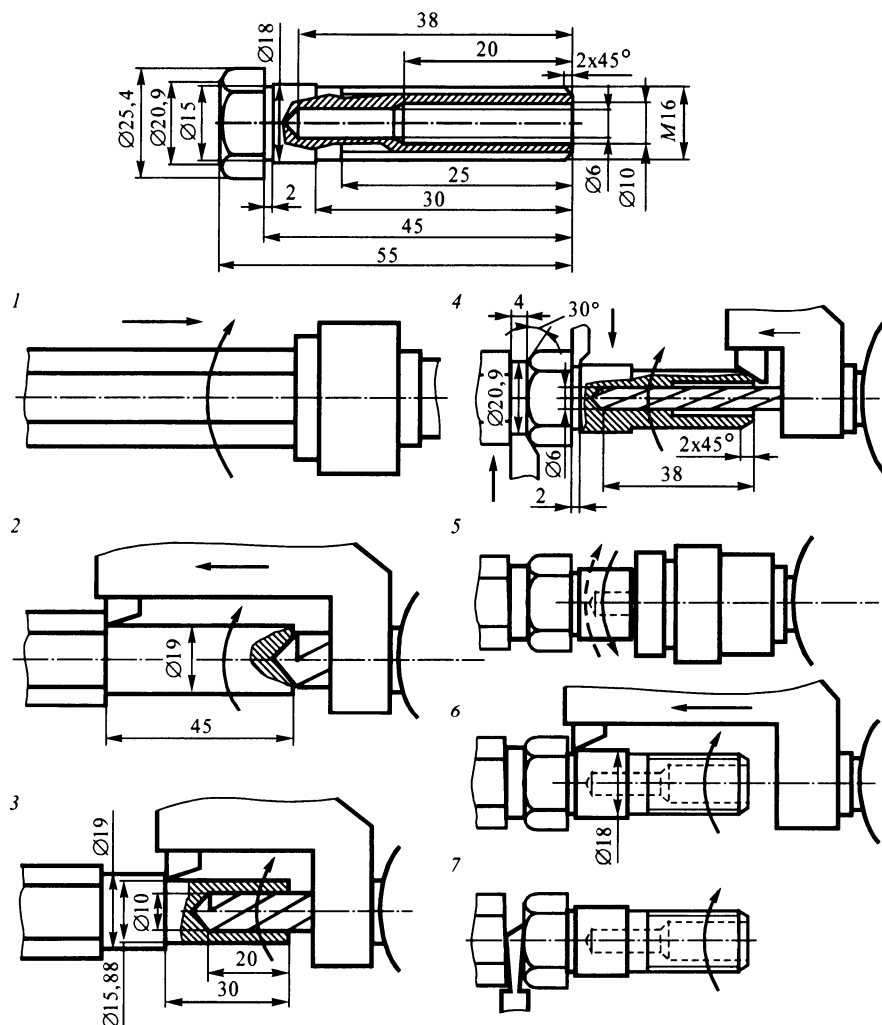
Схема обработки детали на токарно-револьверном станке-автомате:
